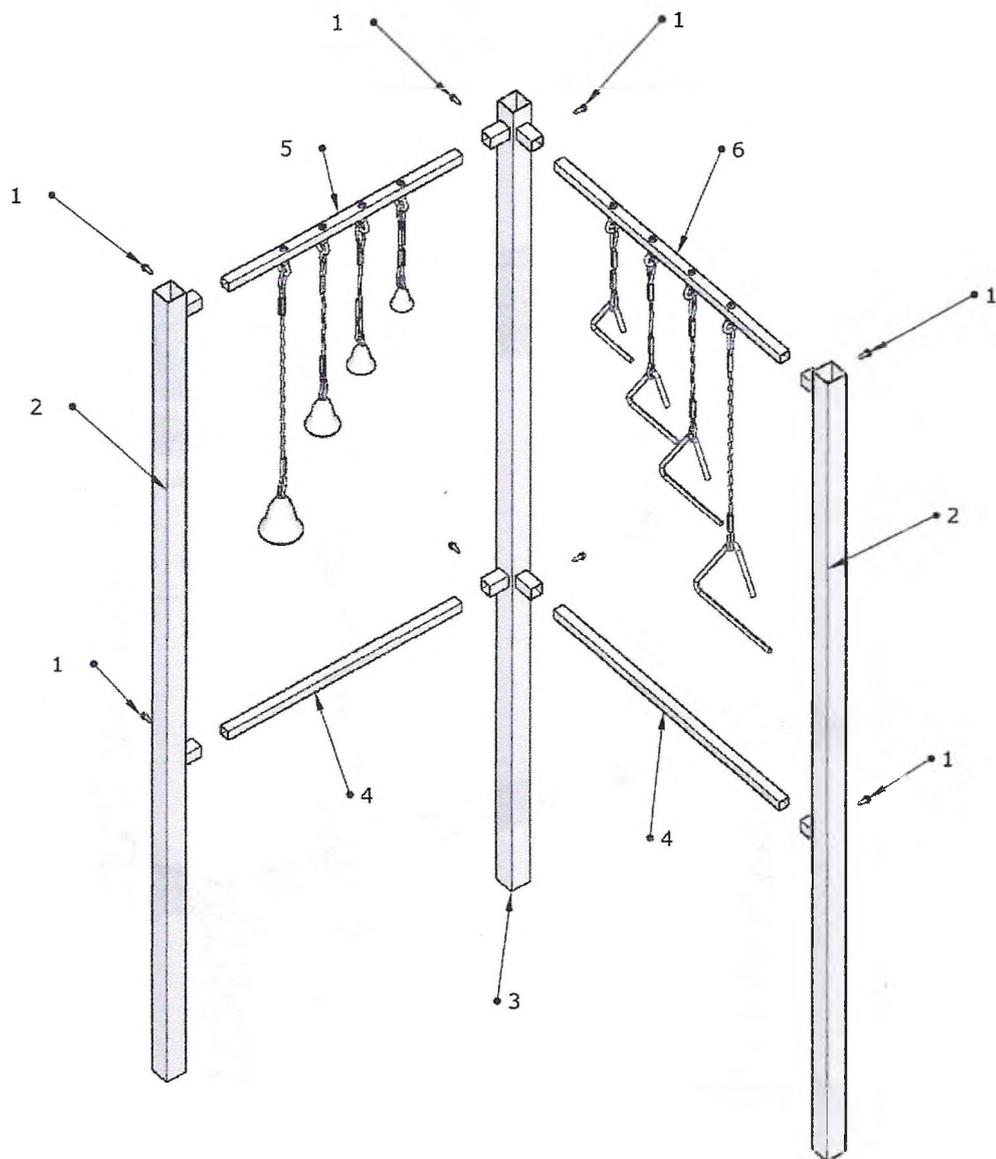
схема расположения деталей Установка «Звонкая капель» (колокольчиков и треугольников)
